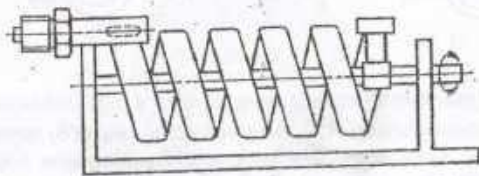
Схема багатовиткової трубчатої пружини
